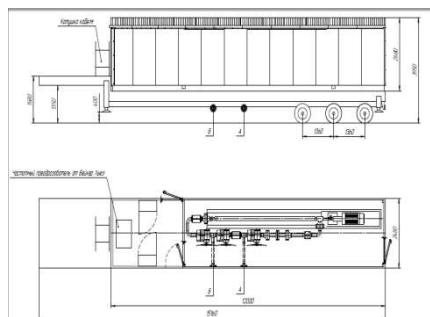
Общий вид автомобильного низкорамного прицепа для установки ГНУ
